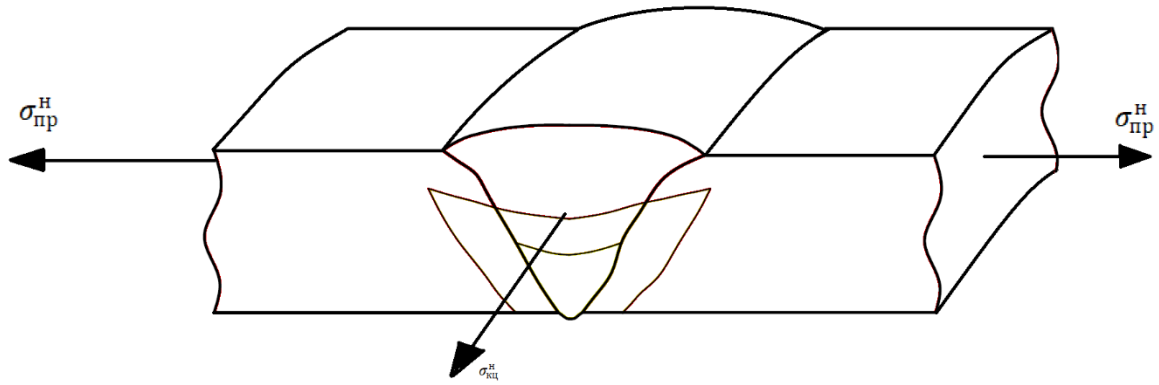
Схема нагружения кольцевого сварного соединения
